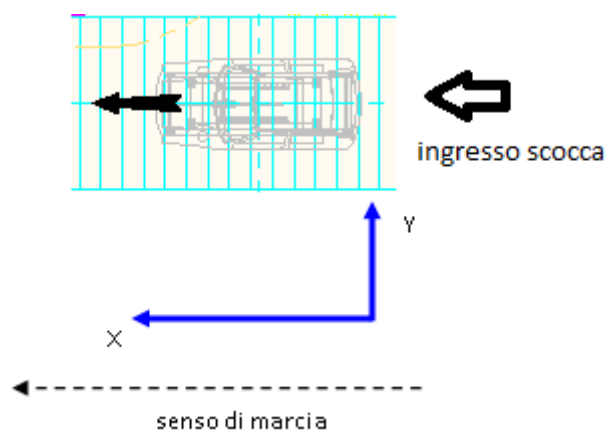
direzione avanzamento tapparella
